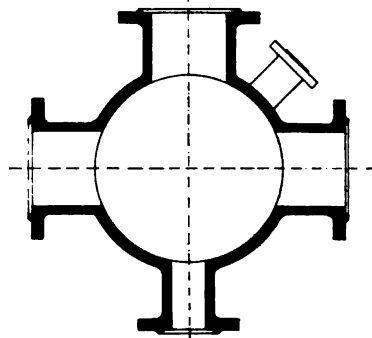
Teilkasten nach vier Richtungen mit Grundablaß. (Lahr.)
